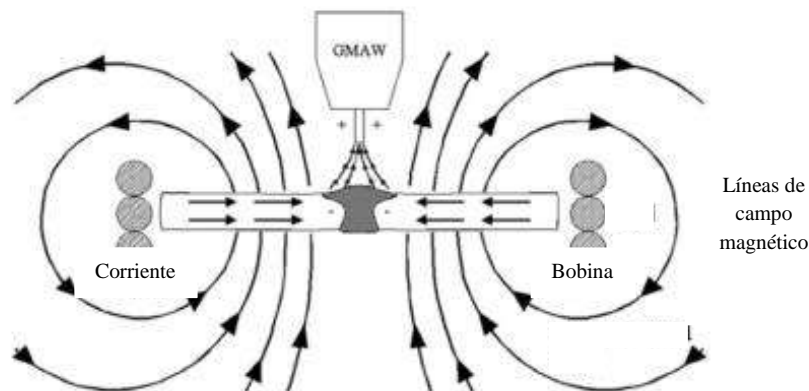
Esquema de un campo magnético inducido durante la soldadura [28].
